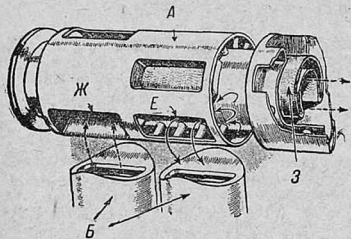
Схема циркуляции горячей смеси между клапанной трубой Мак-Ларена и гильзами цилиндра
